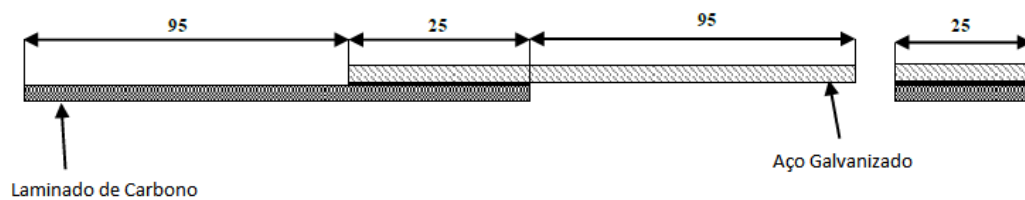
Ilustração da geometria da junta de sobreposição simples de CFRP/HSS.
